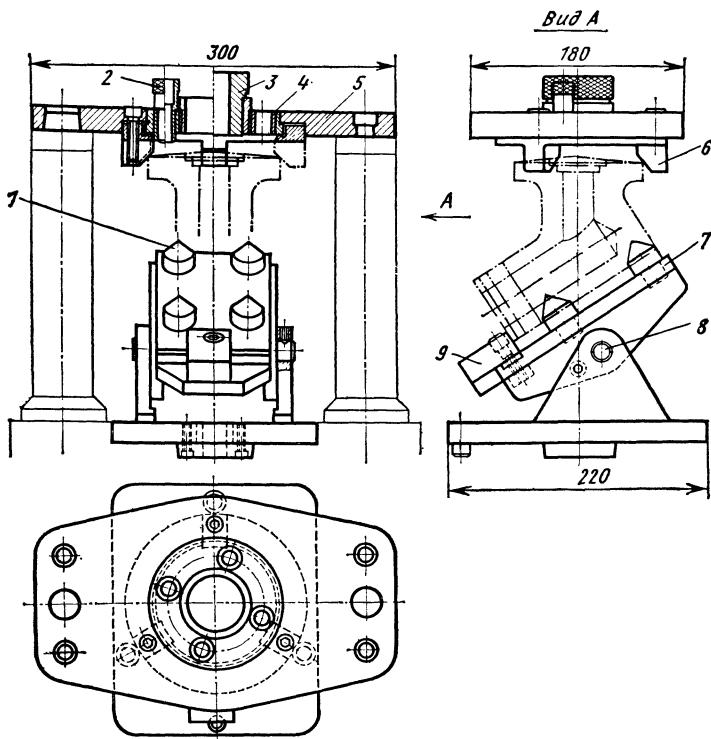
Наладка скальчатого кондуктора для обработки пяти отверстий
